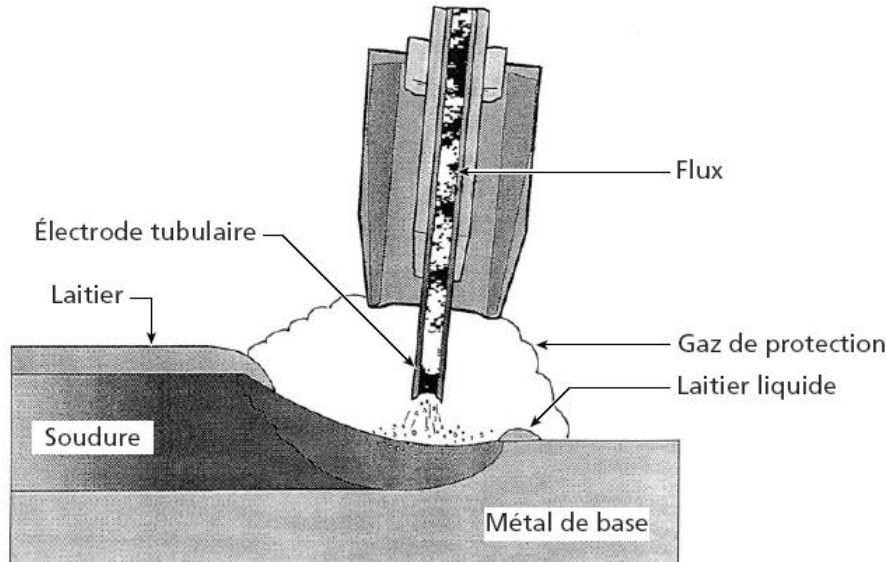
Soudage avec fil fourré et gaz de protection
